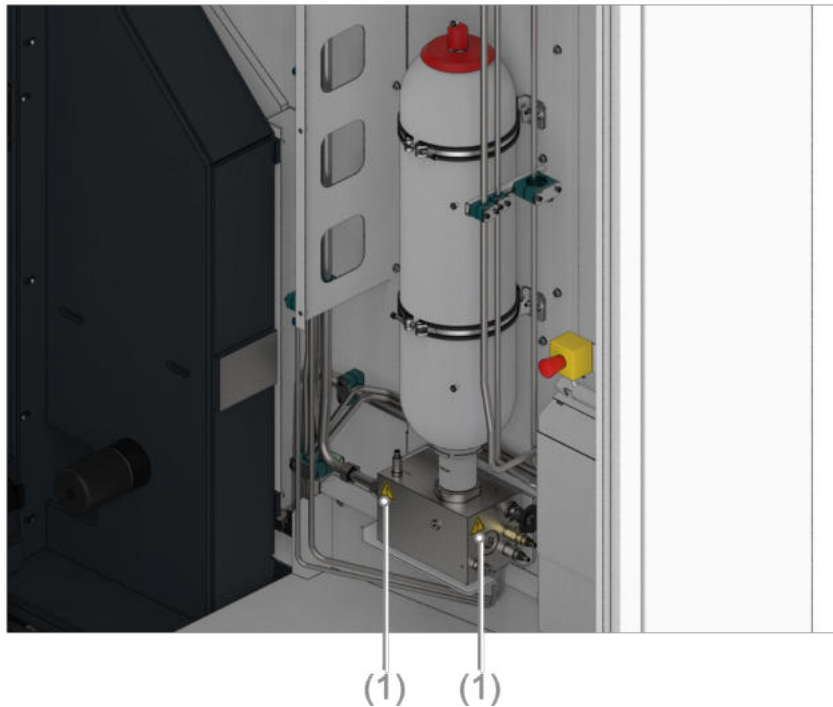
Steuerblock des Gewichtsausgleichs im Maschinenraum
